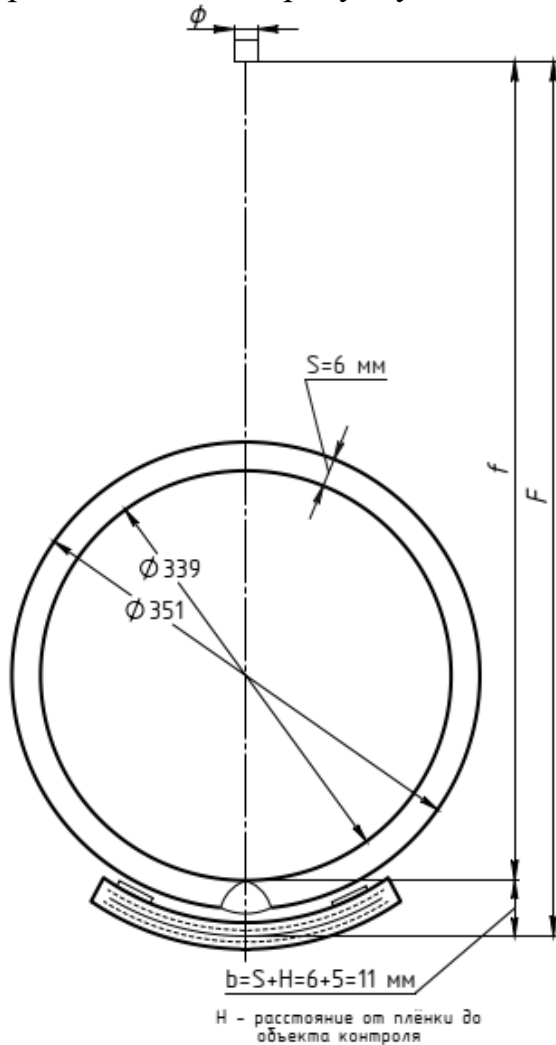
Схема контроля продольного сварного шва
